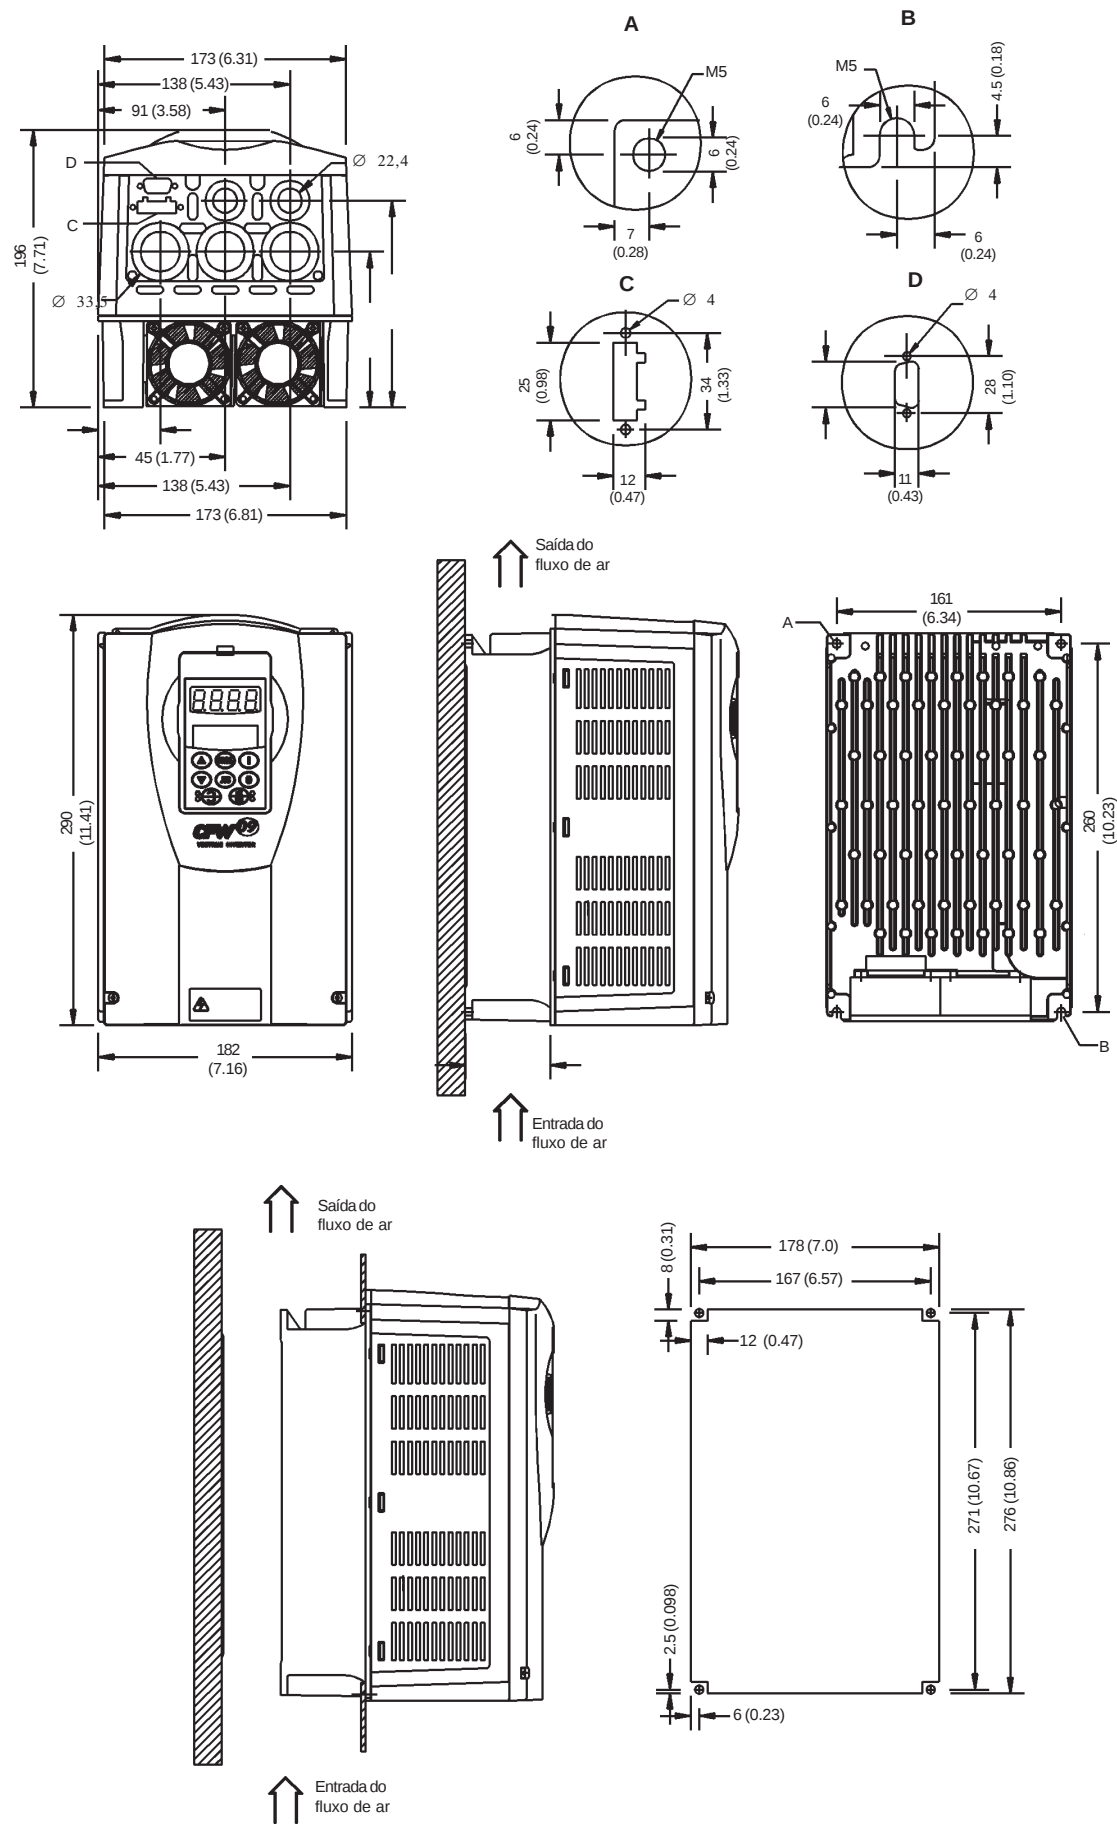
Mecânica 2 - Dimensões em mm (polegadas)
